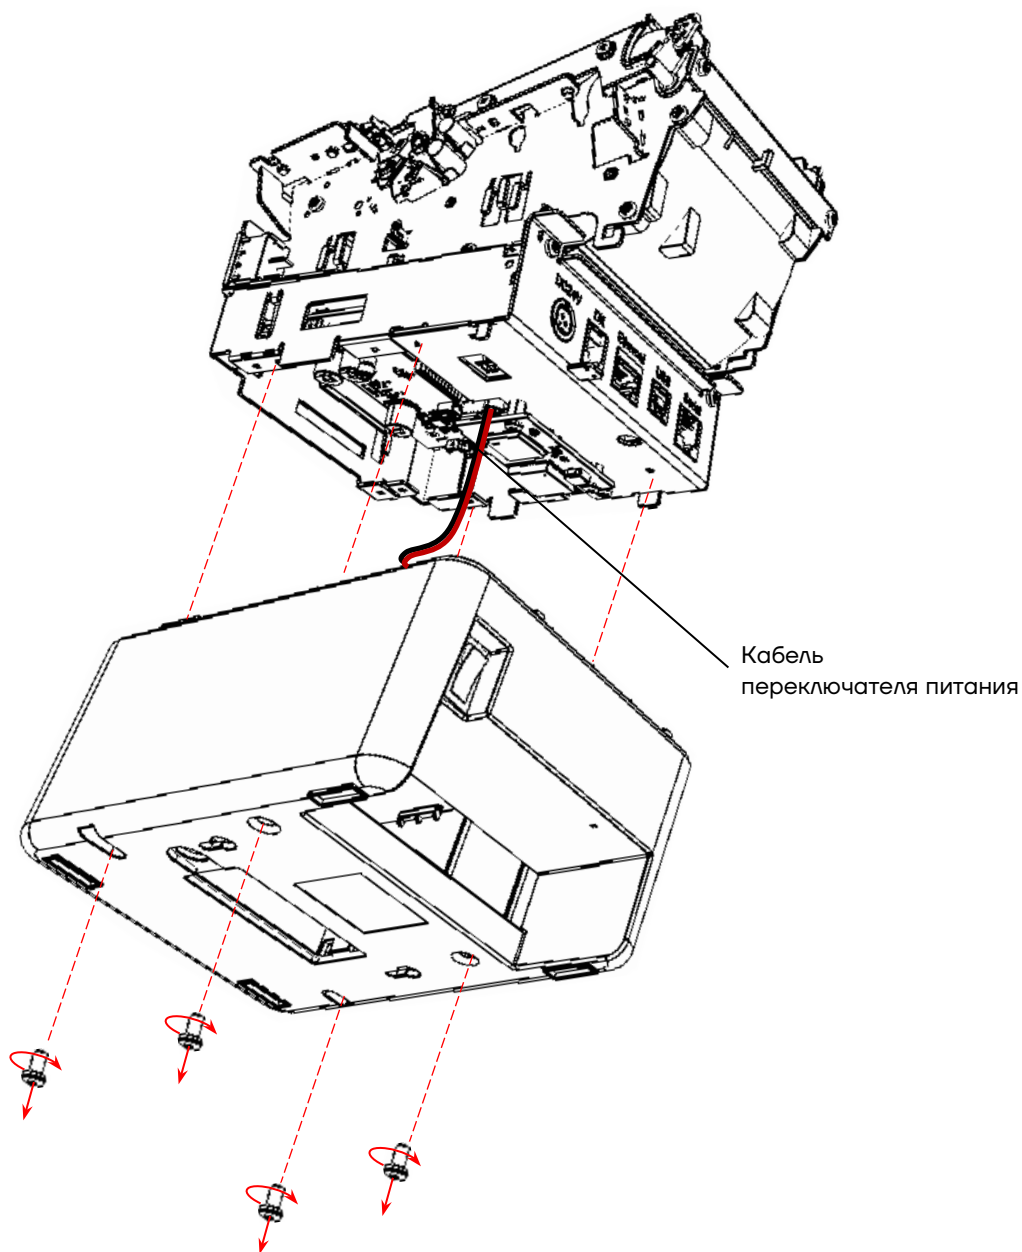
Отделение нижней части корпуса от печатающего устройства
